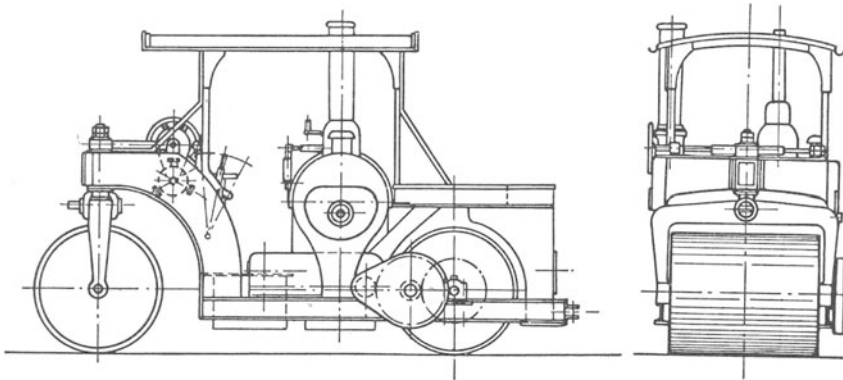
Dampf-Tandem-Walze der Krauß-Maffei A.-G., München.
